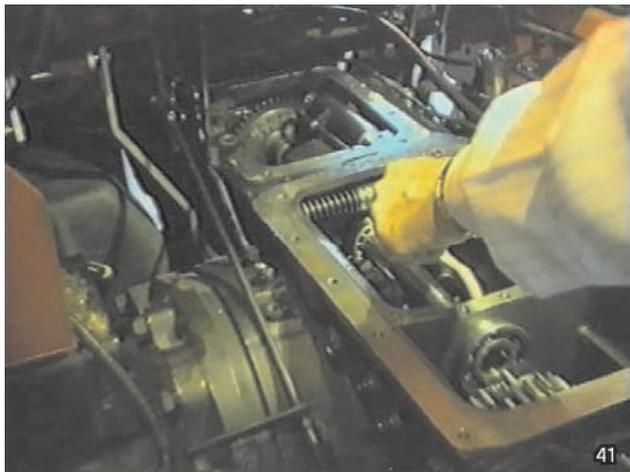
Dégager l'arbre arrière de la P.d.F. vers la partie arrière.
